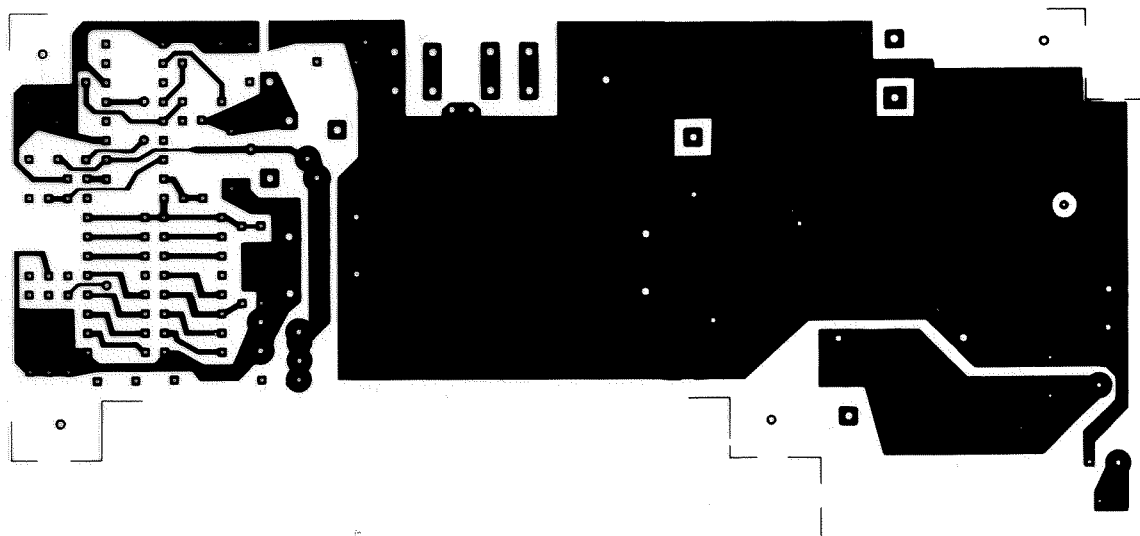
/13.4-10: Componentenzijde 15-V-print.
